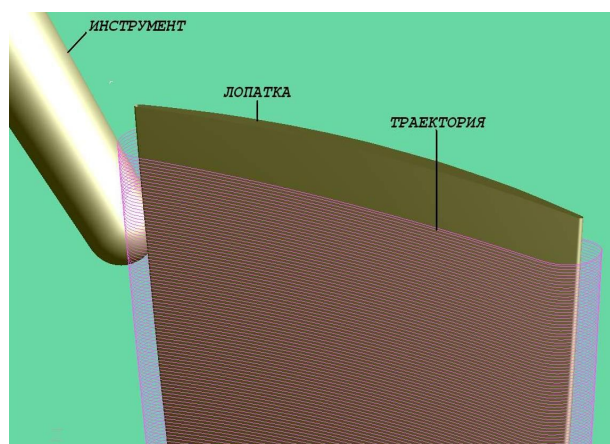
Формообразование пера лопатки моноколеса спиральным высокоскоростным фрезерованием
